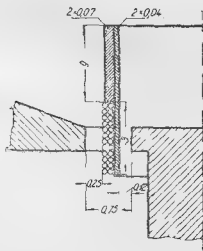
Порядок намотки и основные размеры звуковой катушки
